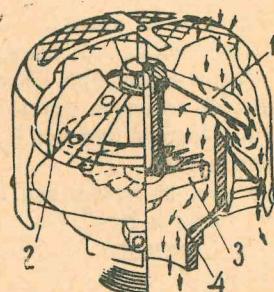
Центробежный воздухоочиститель с подвижным ротором
